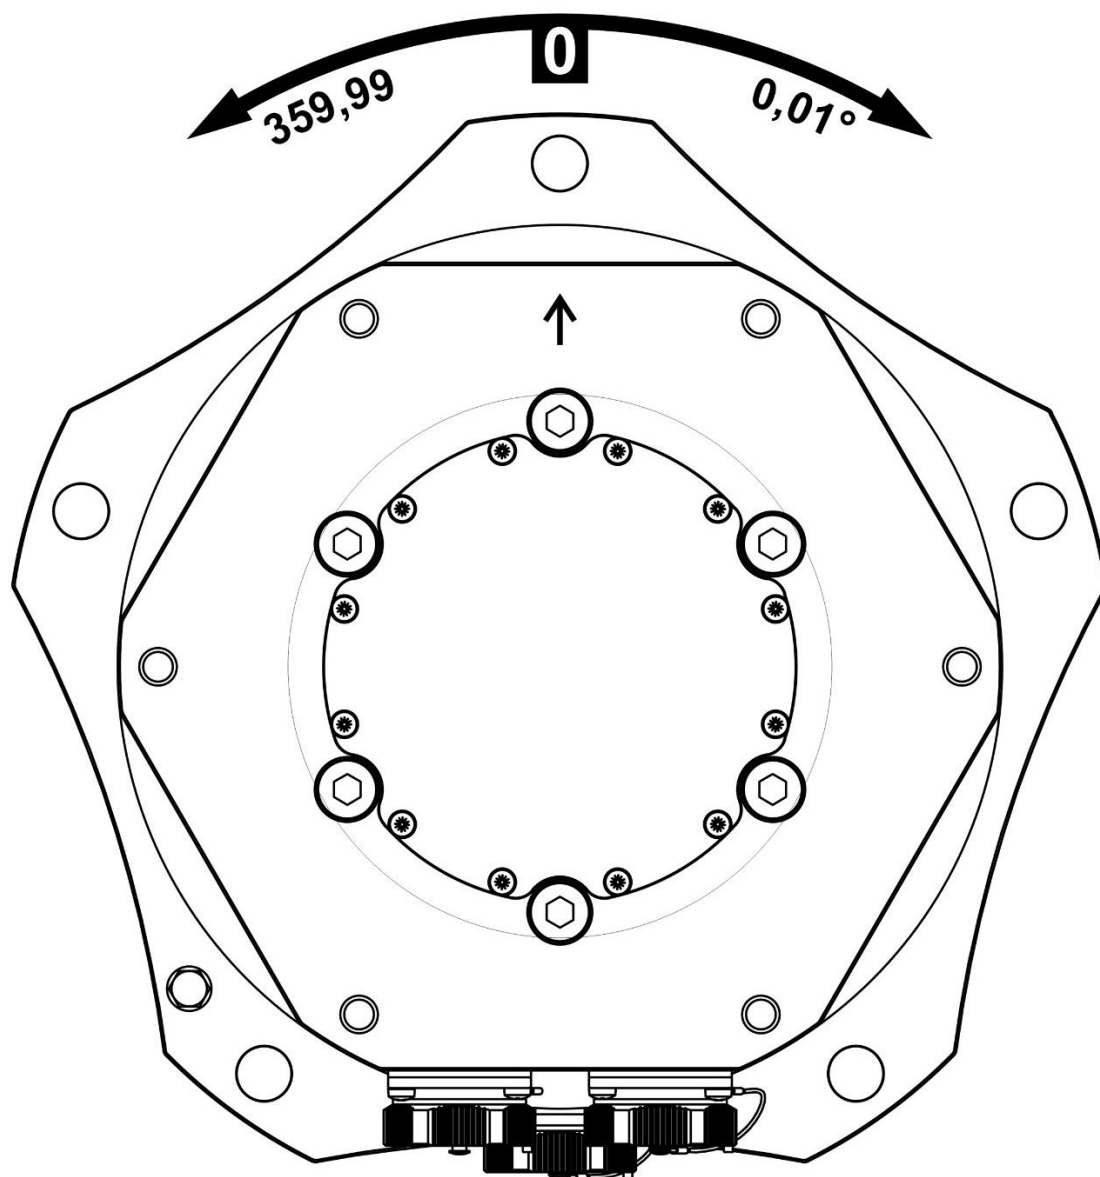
Позиционный чертеж опорно-поворотного устройства.
